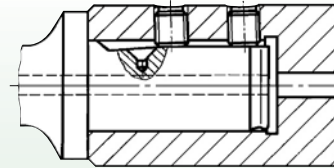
Хвостовик сверла по DIN 6595/ISO 9766 и крепление с помощью двух винтов с плоским торцем.
